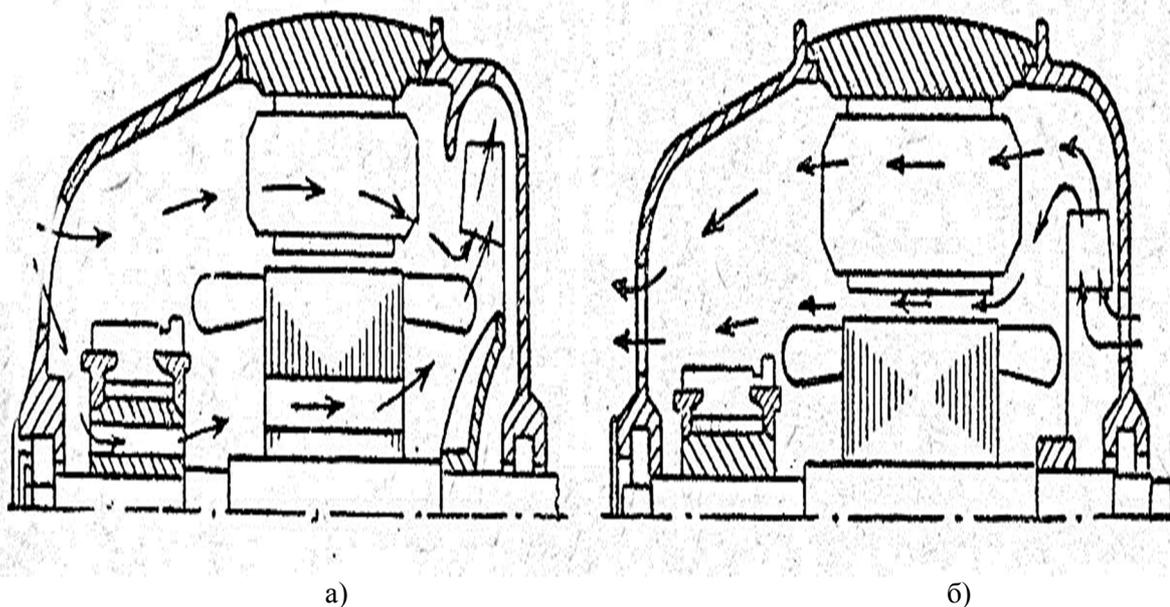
Схема всасывающей и нагнетательной вентиляции
